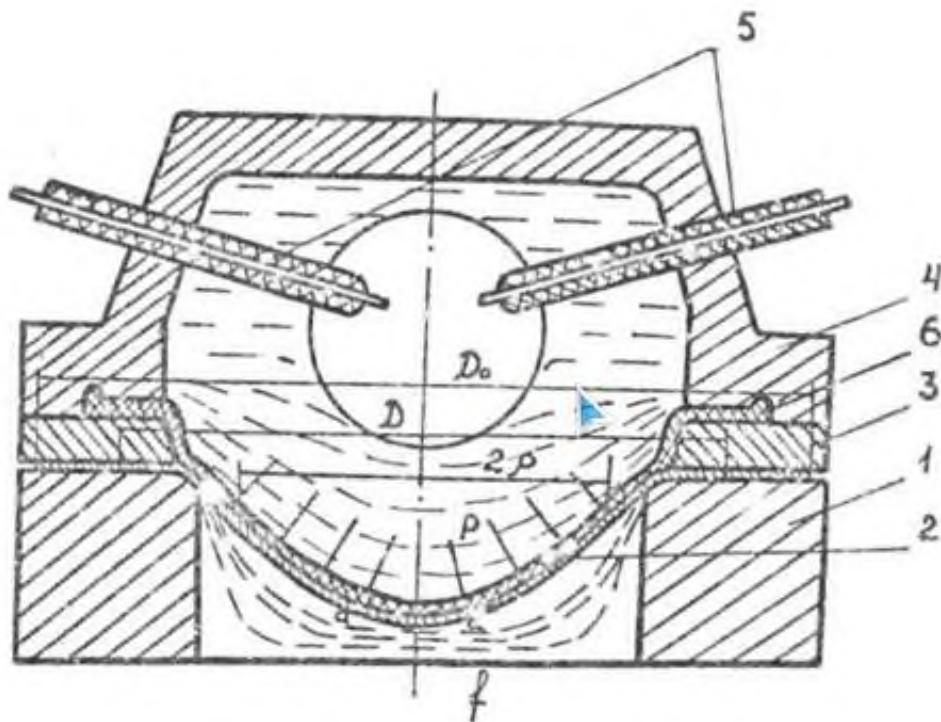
Схема ЕГШ-витягування: 1 – матриця-кільце; 2 – кругла заготовка; 3 – притисна плита; 4 – розрядна камера; 5 – електроди; 6 – діафрагма
